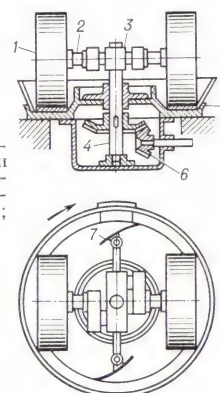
Бегуны: 1 — катки; 2 — полусоск катков; 3 — водило; 4 — центральный вал; 5 — чаша; 6 — привод; 7 — скребки.
